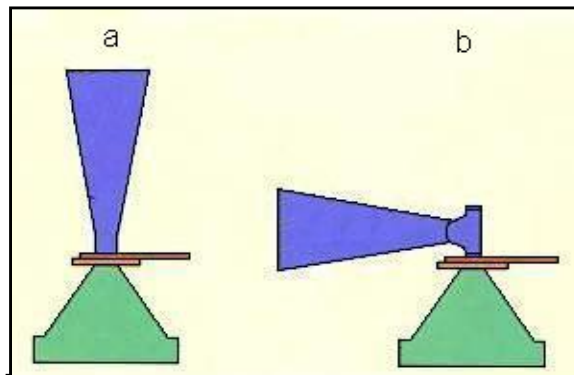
Diferencias en los procesos de soldadura ultrasónica. (a) para plásticos, (b) para metales.
